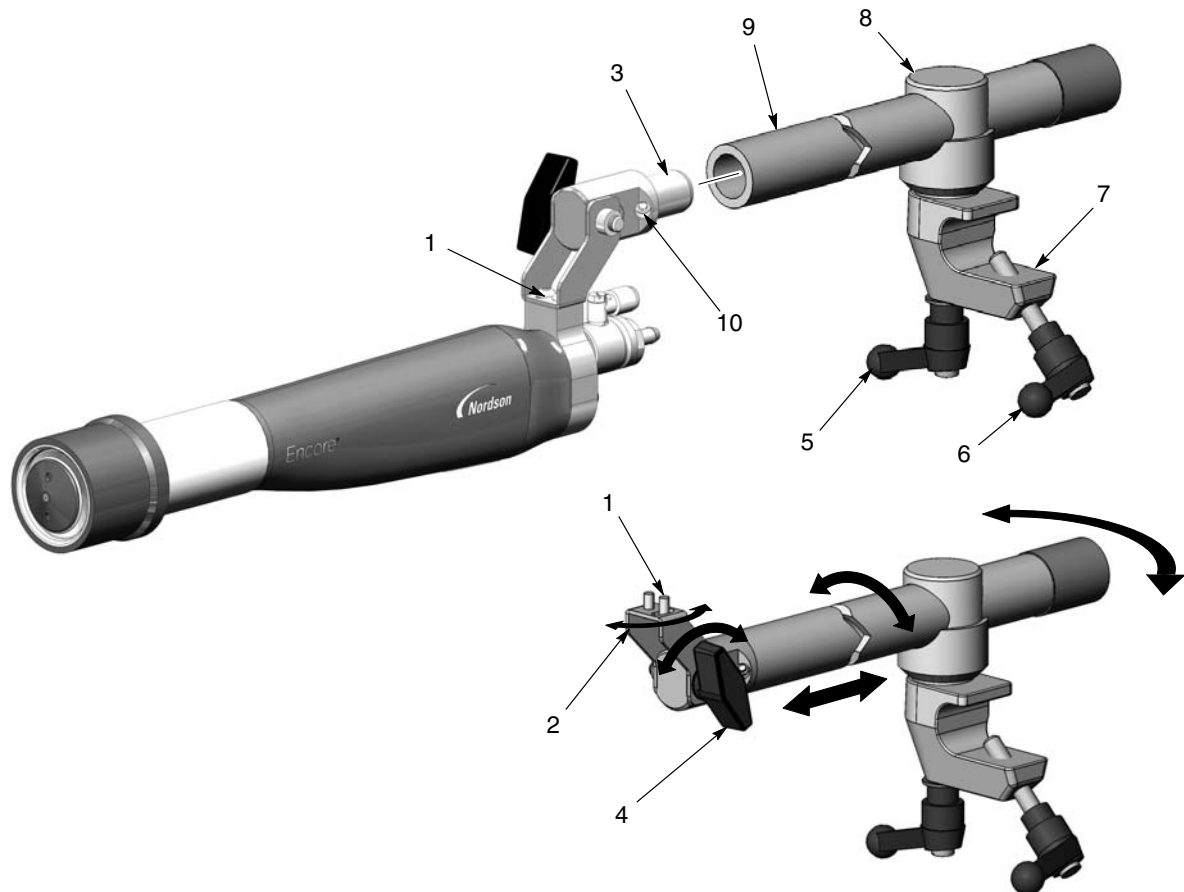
Standardmontage der Pistole an einer Montagestange
